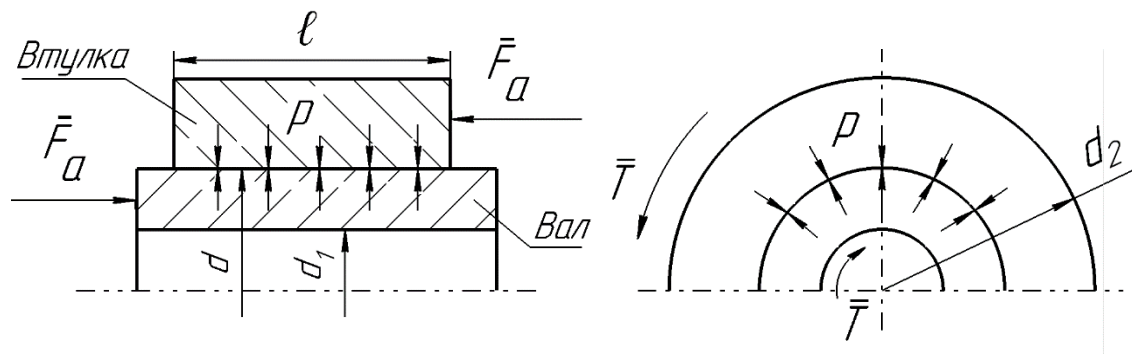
Прессовое соединение после сборки: d и l – соответственно, номинальный диаметр и длина посадочной поверхности вала и втулки;
